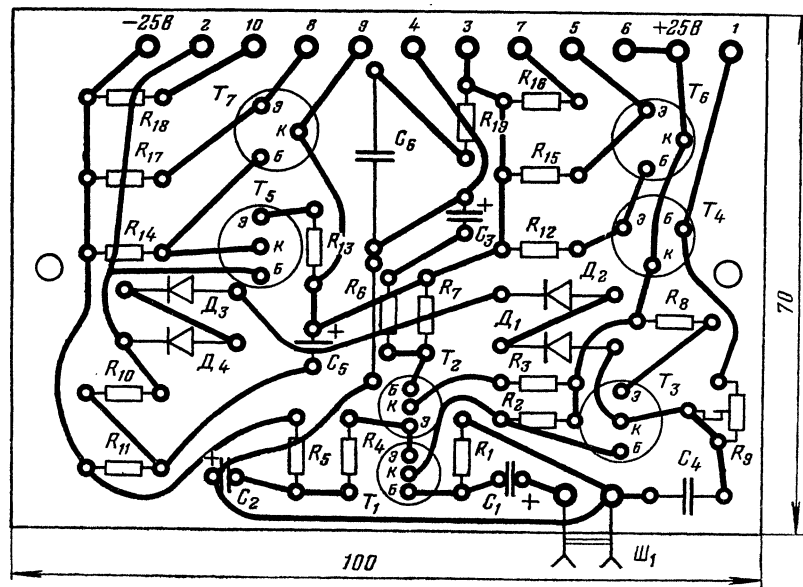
Печатная плата и схема соединения деталей усилителя.
